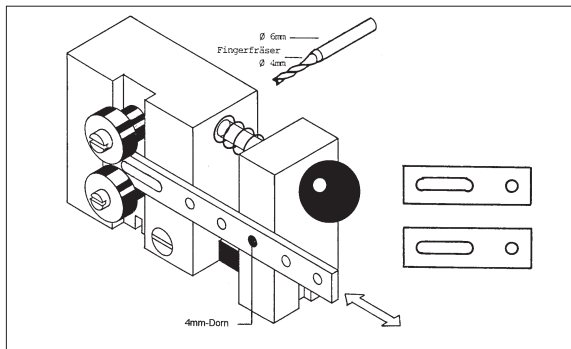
Fräsen von Langlöchern mit der UMT-Fräsvorrichtung
